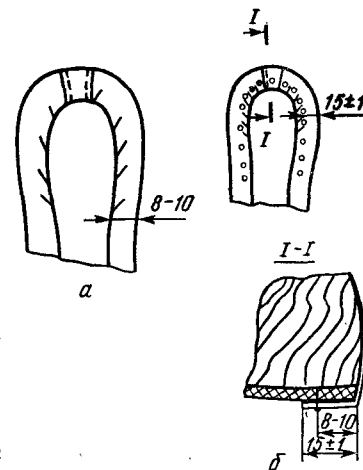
Схемы затяжки пяточной части заготовки верха обуви
